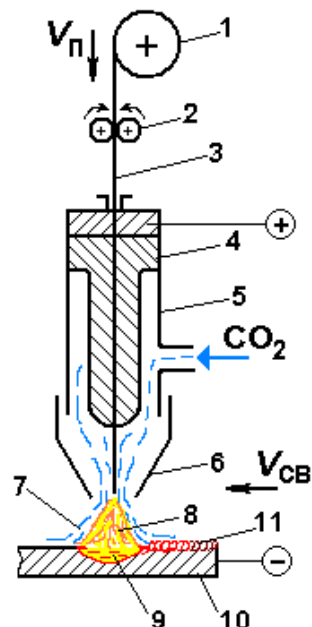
Схема сварки в углекислом газе: 1 – кассета с проволокой; 2 – механизм подачи; 3 – проволока; 4 – токоподводящий мундштук; 5 – корпус горелки; 6 – сопло; 7 – атмосфера защитного газа; 8 – дуга; 9 – ванна жидкого металла; 10 – свариваемый металл; 11 – шов
